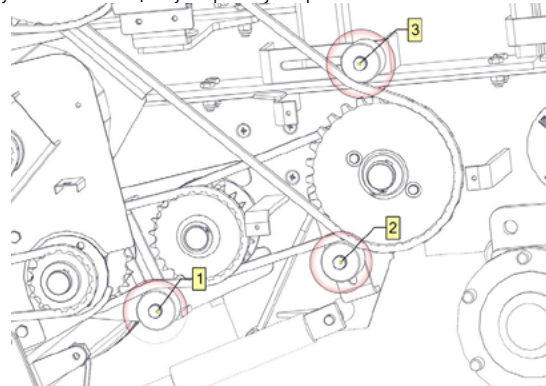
Регулировка натяжения цепей с левой стороны пресс-подборщика
